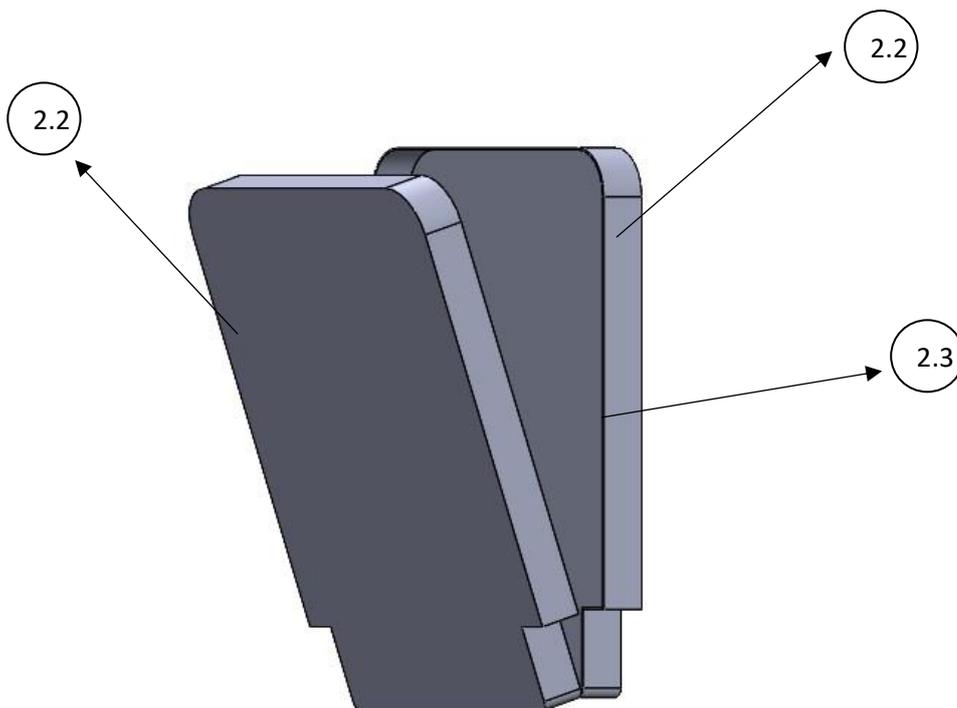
Ensamblaje final del subconjunto 1.1
